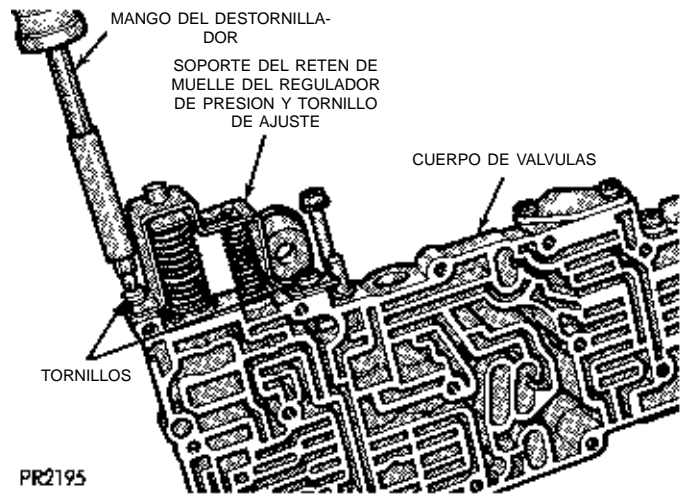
Soporte del tornillo de ajuste y regulador de presión
